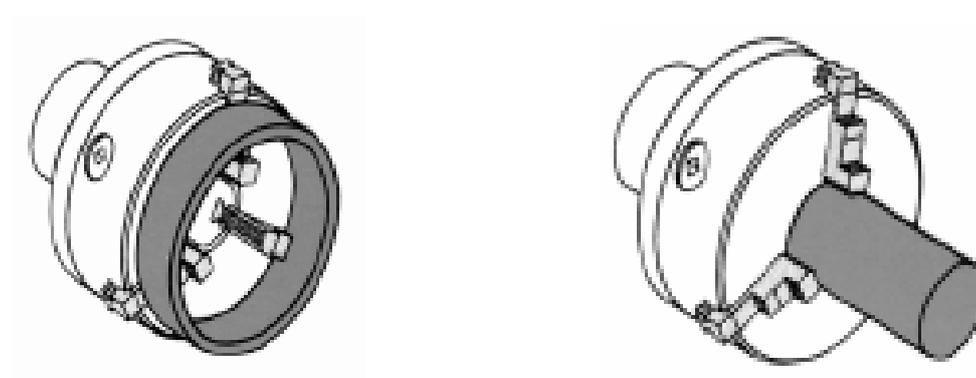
Exemplo de aplicação da placas de 3 castanhas
